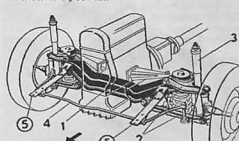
Задний мост автомобиля «Мерседес-Бенц» 1960 года: 1 — дифференциальный корпус; 2 — поворачивающаяся опора со спиральными рессорами; 3 — выравнивающая пружина; 4 — гидравлический амортизатор.
